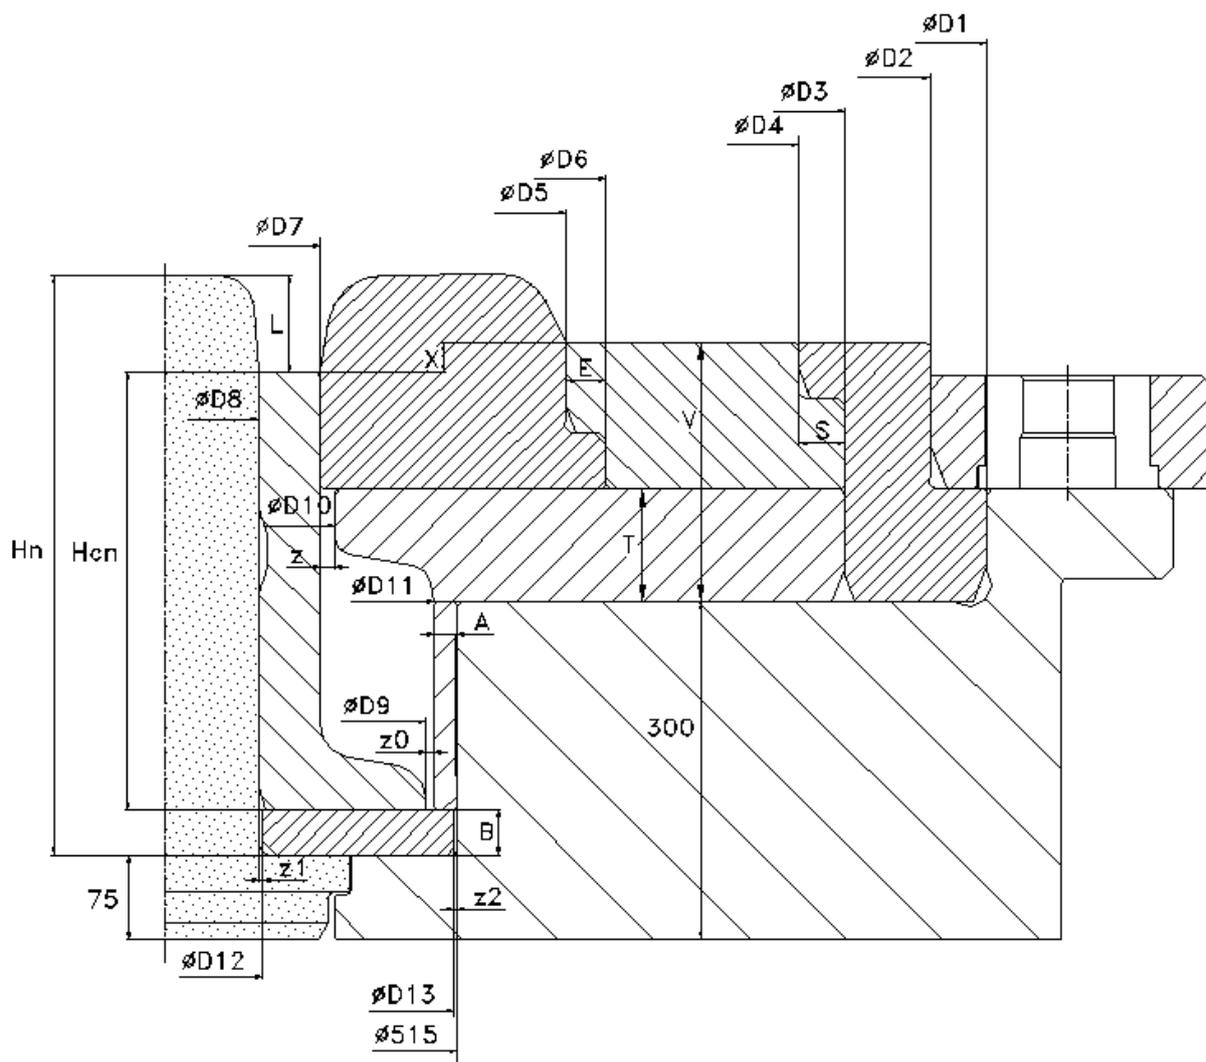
Схема размеров инструмента сборочного чертежа формовочного пресса (нижний штамп)
